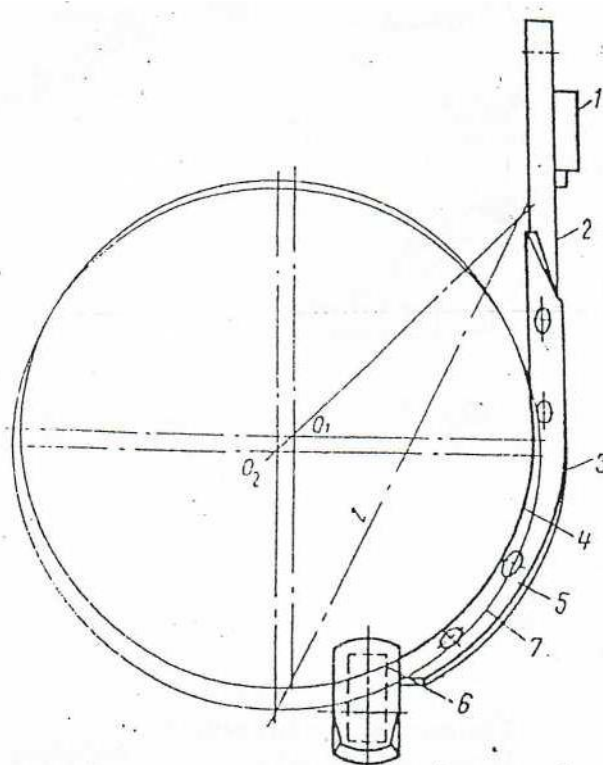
Робочий орган розпушувача [16], вид спереду
